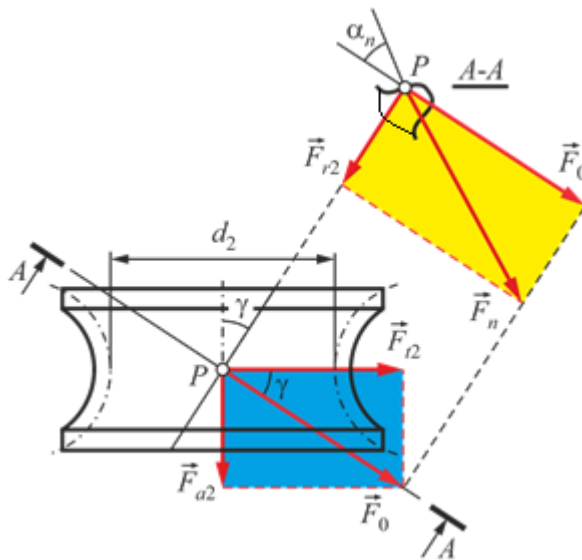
Зусилля на зубцях черв'ячного колеса.
